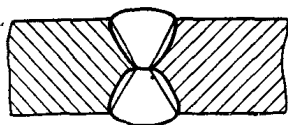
Сварное соединение стыковое с двумя симметричными скосами двух кромок двустороннее
